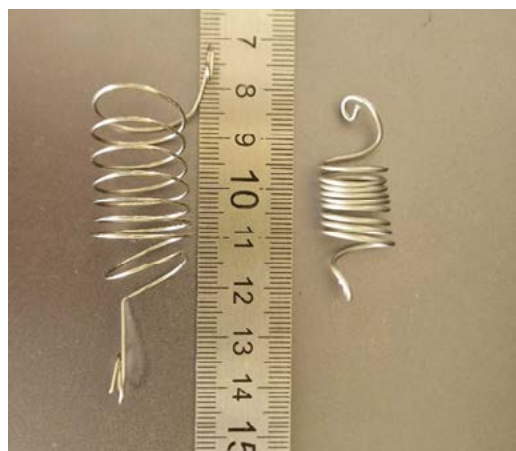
Пружины из сварочной нержавеющей (слева) и пищевой нержавеющей (справа) проволоки [1, с. 18].
